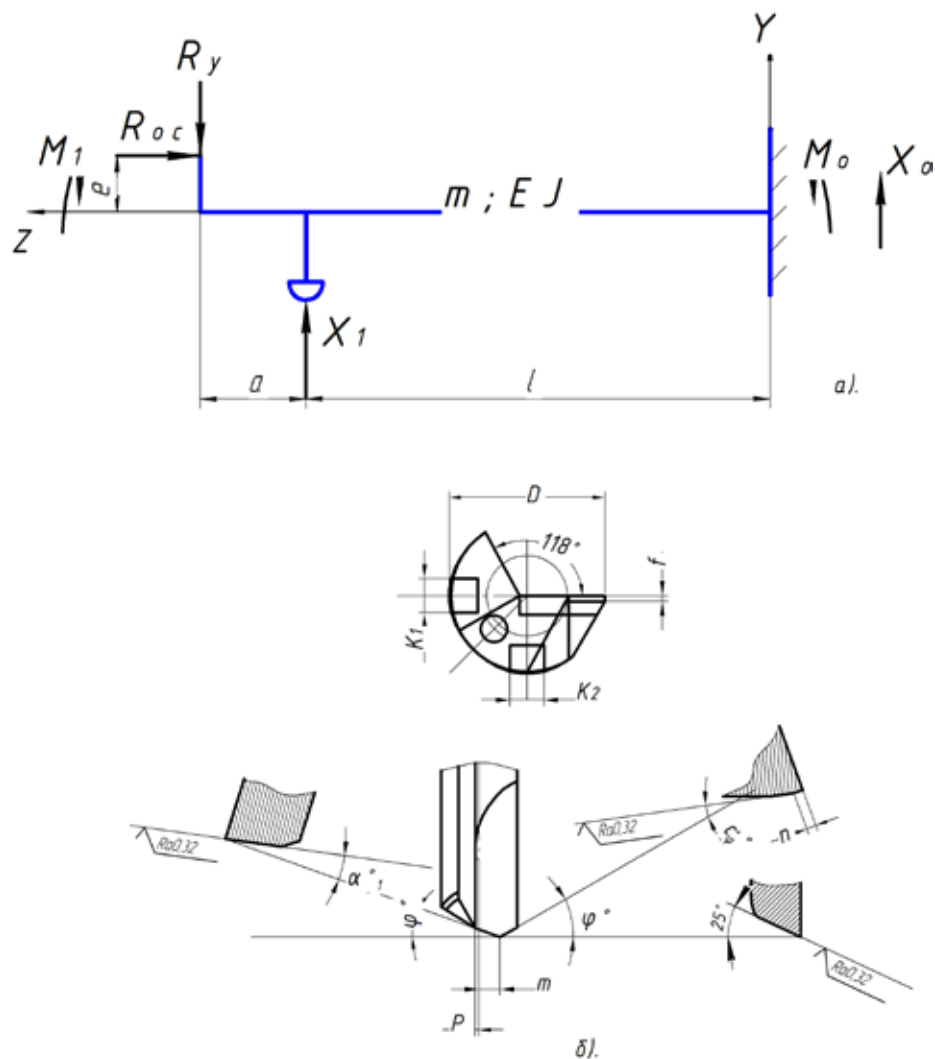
Схемы: а - расчета смещений инструмента при сверлении; б - режущей части сверла, одностороннего резания
